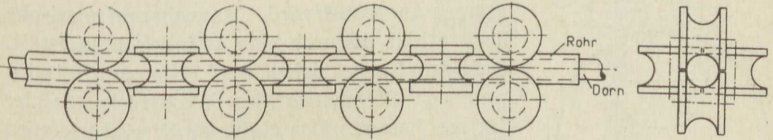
Kontinuierliches Röhrenwalzwerk.
